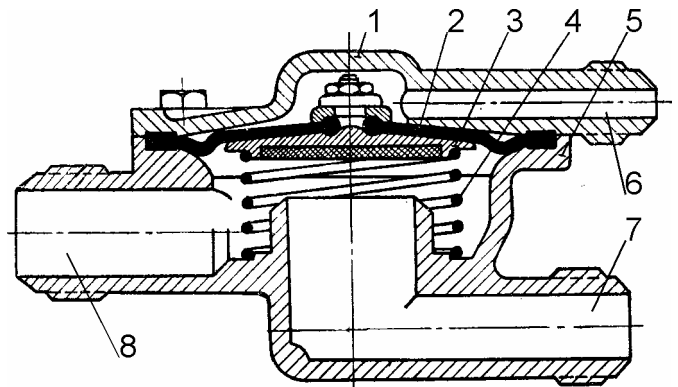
Клапан увімкнення наддування (МиГ-21/23/25/29): 1 — кришка; 2 — мембрана; 3 — клапан; 4 — пружина; 5 — корпус; 6 — штуцер підведення командного палива; 7 — штуцер лінії наддування; 8 — штуцер лінії дренажу
